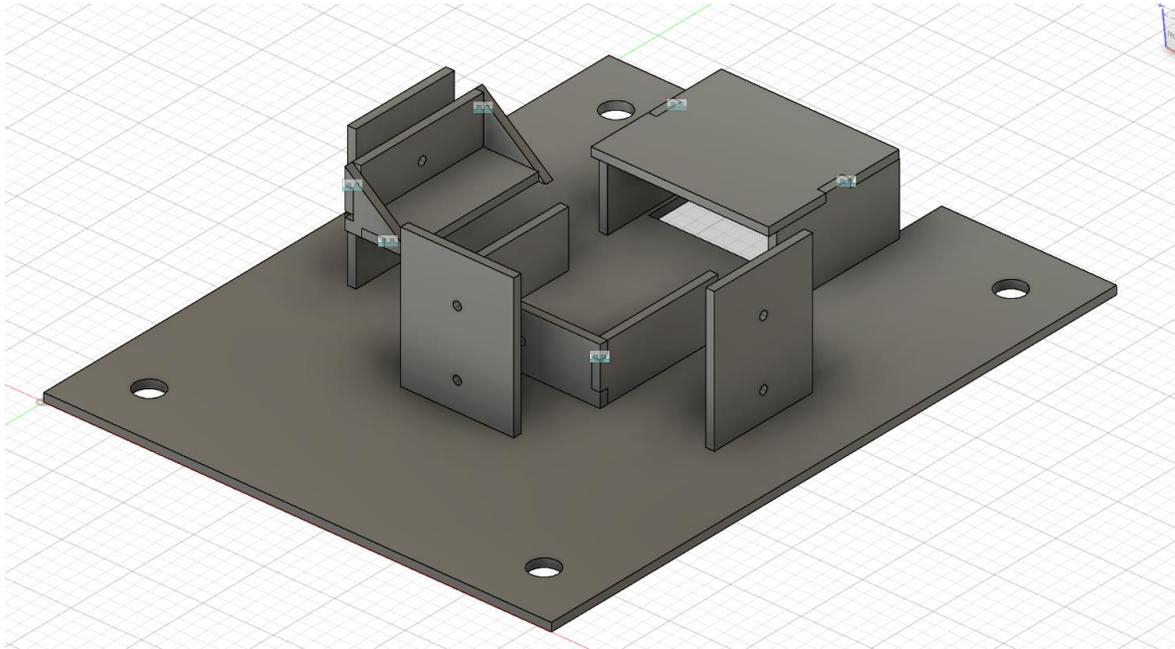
Explosionado del diseño solución B en Autodesk Inventor®. Fuente: Autores.
